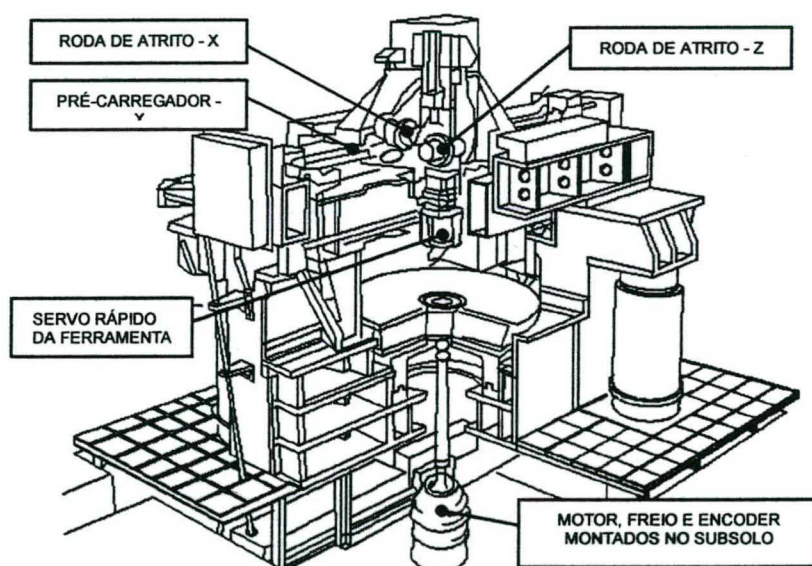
Large Optics Diamond Turning Machine [15].
